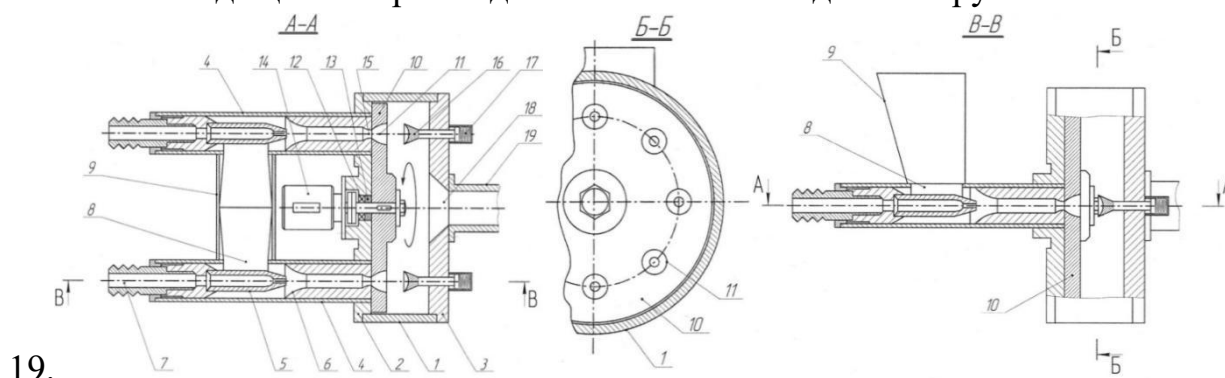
Гидроударно-кавитационный смеситель: 1 – рабочая камера; 2 и 3 – стенки рабочей камеры; 4 - эжекционные камеры; 5 - эжекционные сопла; 6 – конфузоры; 7 - подводящие патрубки; 8 - боковые окна, 9 - загрузочный бункер; 10 - диск; 11 - концентричные отверстия; 12 - подшипник; 13 - уплотнение; 14 – электродвигатель; 15 – сужающиеся каналы; 16 - отражатели; 17 - пружины; 18 - отводящее отверстие для смеси; 19 - выходной патрубков
